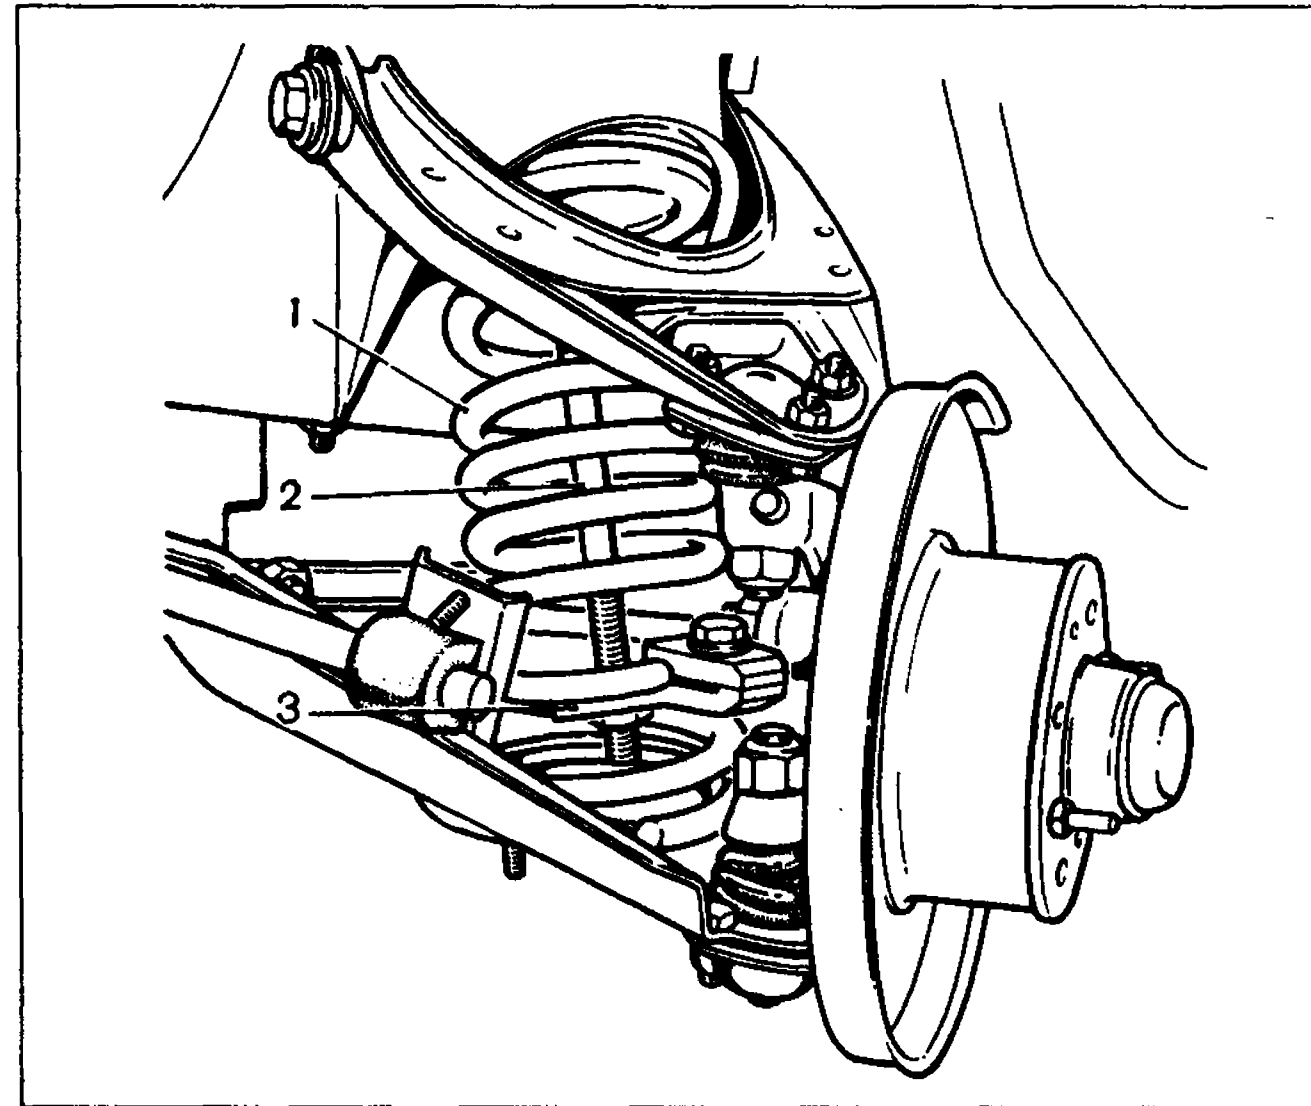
Сжатие пружины приспособлением 67.7828.9504: 1-пружина подвески; 2-винт приспособления; 3-опорная тарелка
